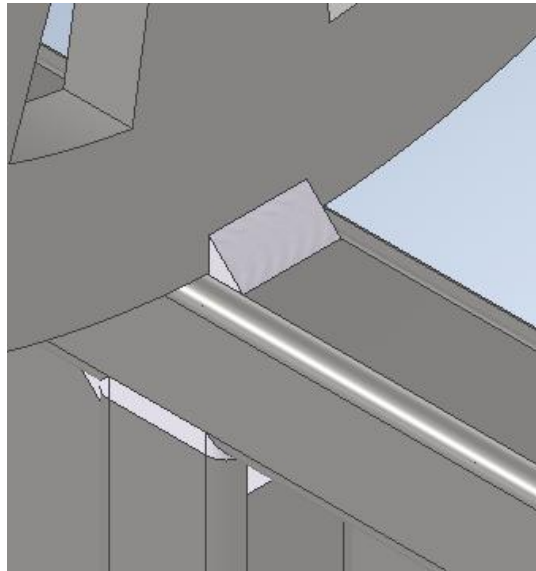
Refuerzo estructural del álabe antes de la modificación.
